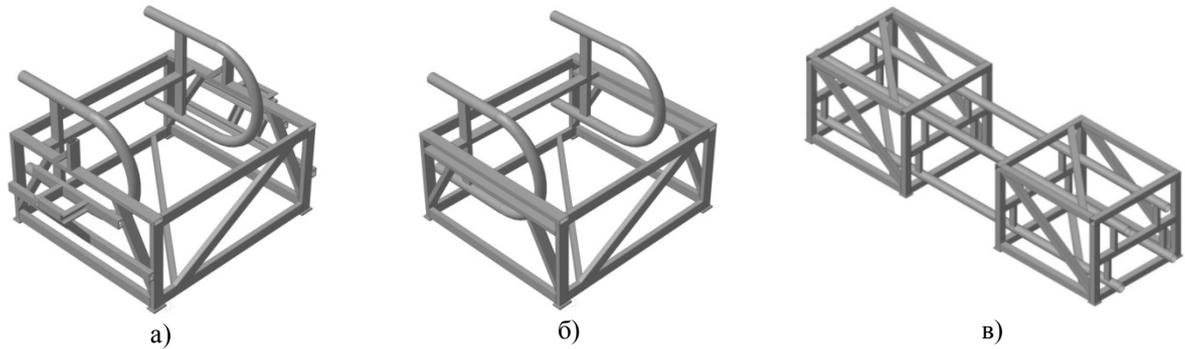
Схемы металлоконструкций конвейера с подвесной лентой:
